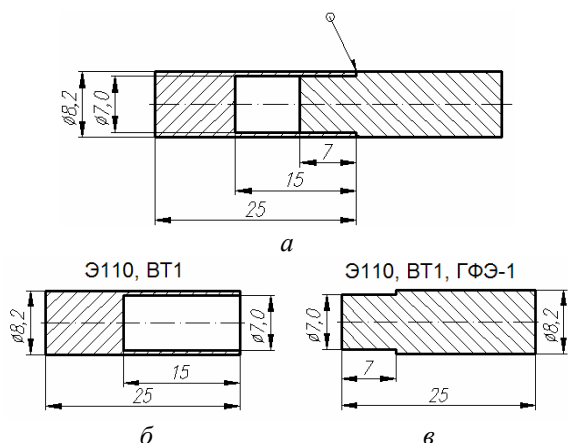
Конструкция изделий для исследования влияния режимов электродуговой сварки в среде гелия на параметры сварных швов
